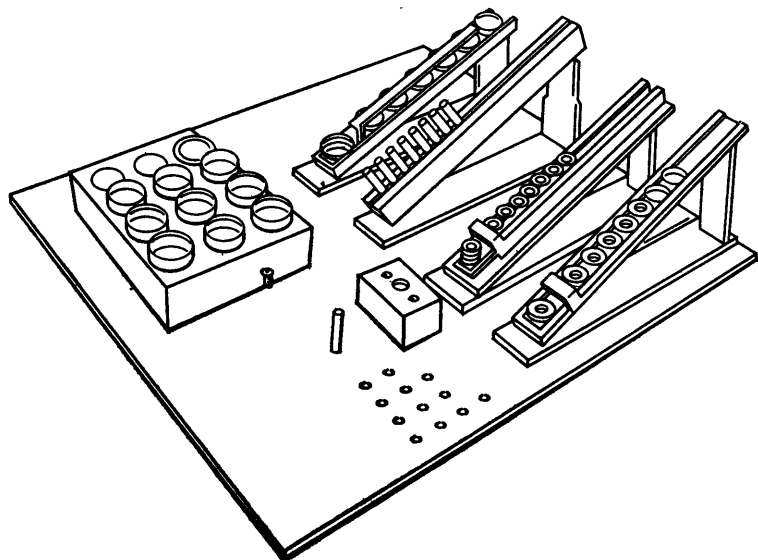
Внешний вид рабочей зоны сборки амортизатора
